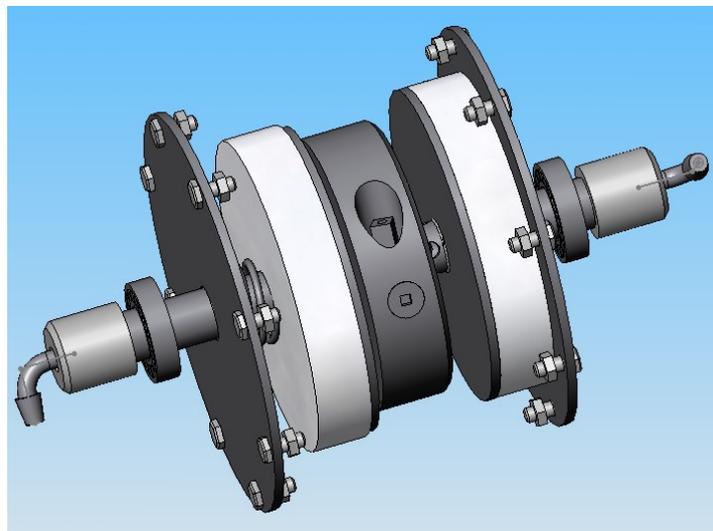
Модель ГРД. Корпус и опоры вала условно не показаны
